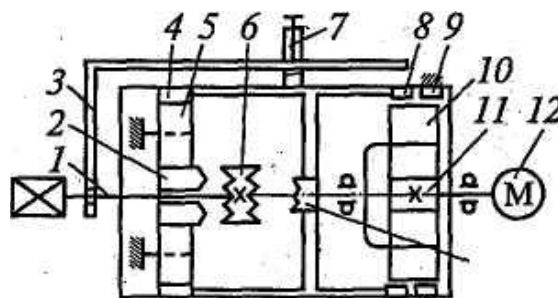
Кинематическая схема резьбонарезной машины
